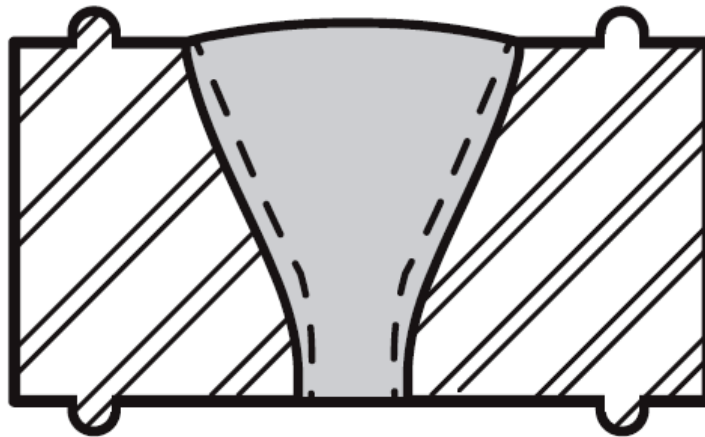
Probeta para Ensayo de Macroataque de Junta Directa a Tope.
